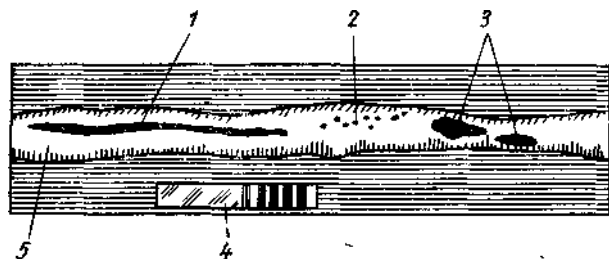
Примерный вид у-снимка участка сварного шва при наличии дефектов.
